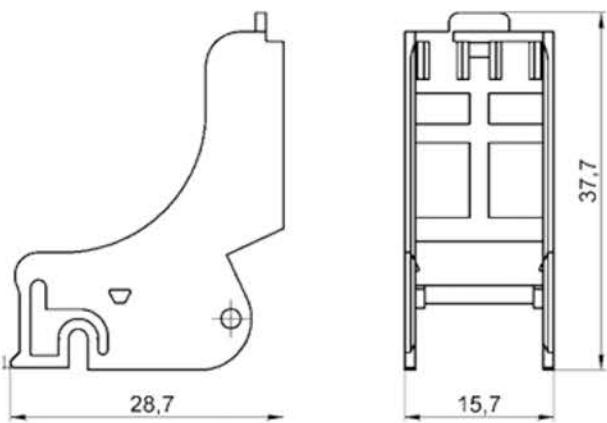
Габаритные, установочные, присоединительные размеры пластикового фиксатора реле OptiRel 46-H1
